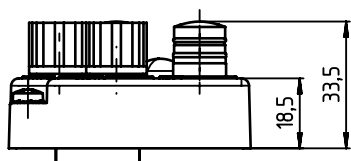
Desenho dimensional BPS com tampa de conexão MK 300
